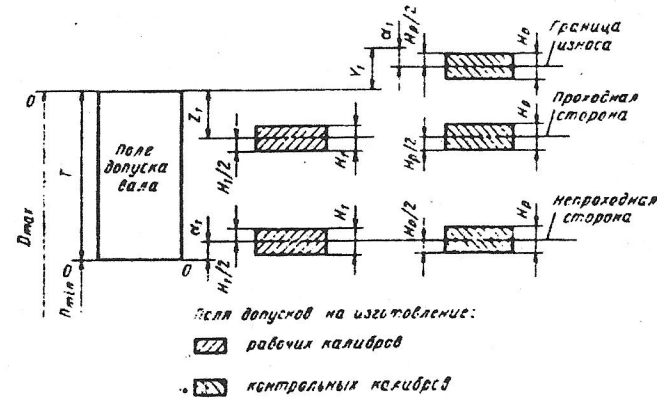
Схема расположения полей допусков калибров для валов
